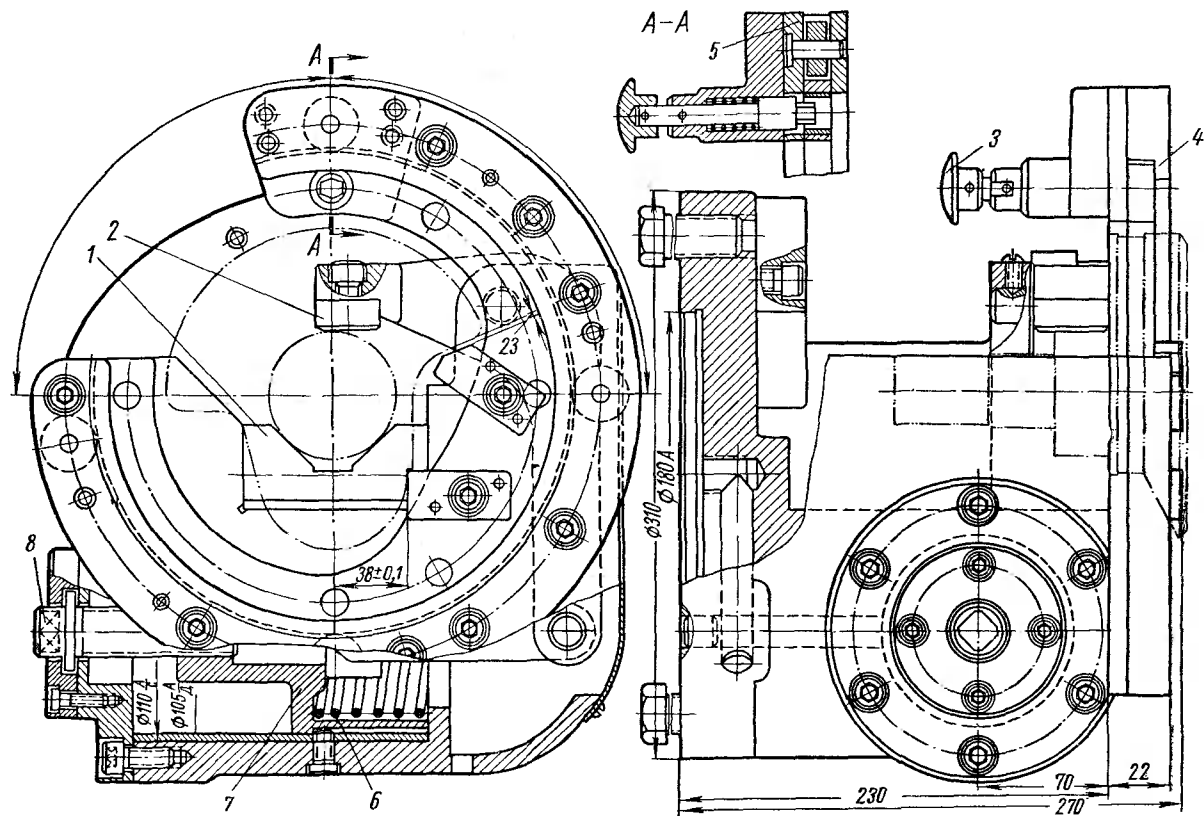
Патрон для установки коленчатых валов при шлифовании шеек
